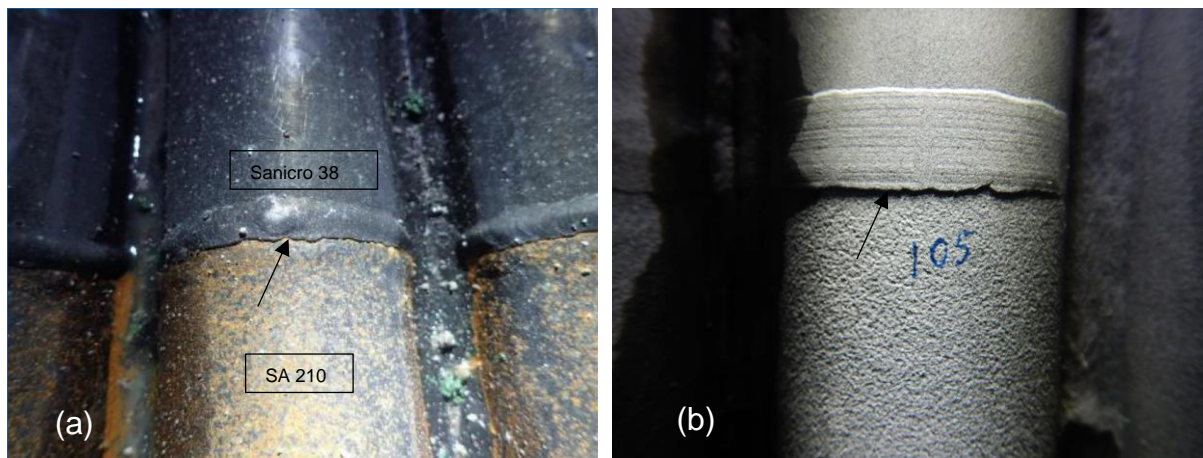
Corrosão galvânica na zona de transição entre tubos protegidos com *weld overlay* com 25%Cr e 18%Cr.
